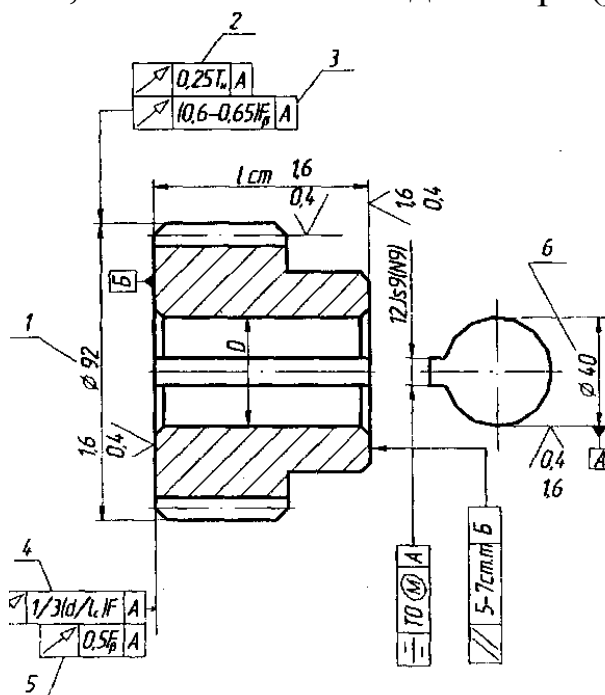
Зубчатое колесо с типовыми требованиями к точности его изготовления
